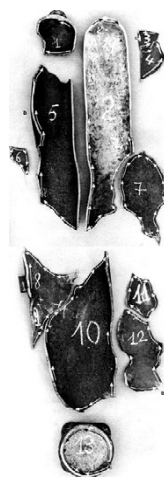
Fragmentos de la rotura de tipo frágil de una botella de acero sin soldadura para gas.
